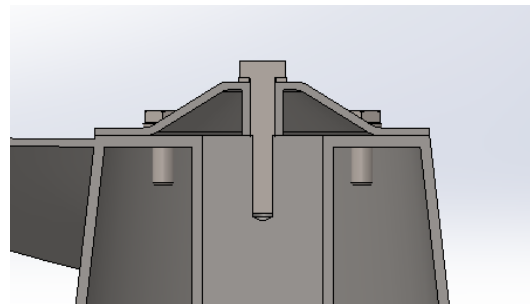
Vista seccionada assemblatge tapa hèlice
